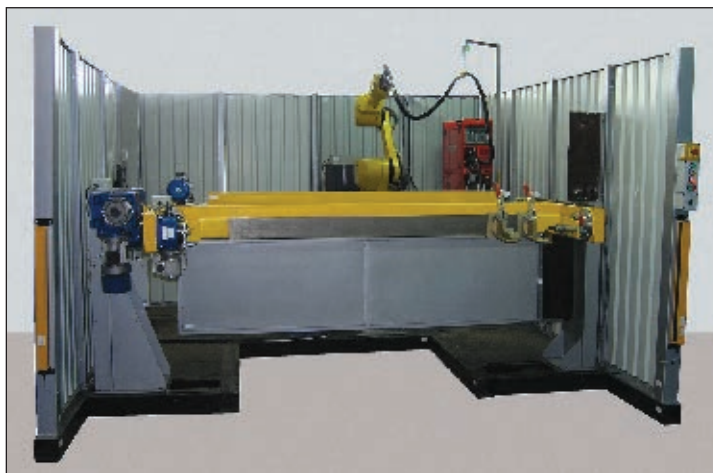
Робототехнологический комплекс РК754 для сварки конвекторов
